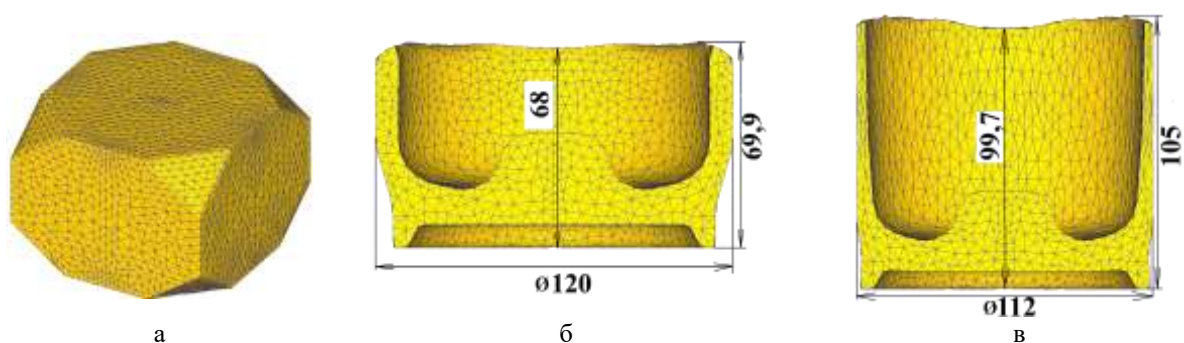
Операційні переходи формоутворення порожнистого виробу з механічним зняттям фасок на вершинах заготовки: а – вихідна заготовка, б – проміжний напівфабрикату після зворотного видавлювання, в – виріб після витягування
